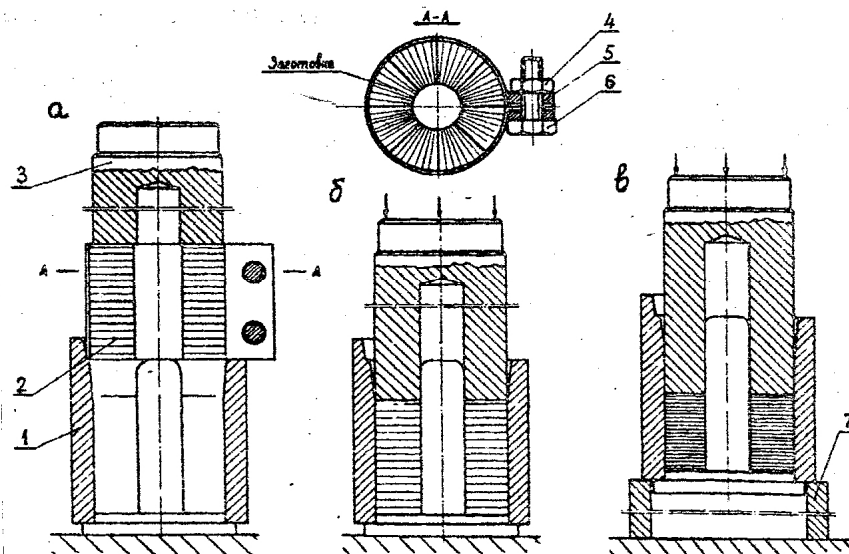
Технология сборки втулки из секторов прессованной древесины:
